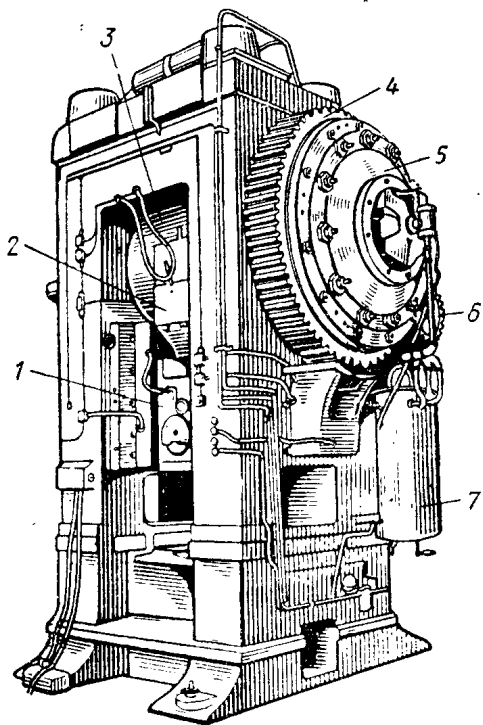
Кривошипный ковочно-штамповочный пресс К-864:
